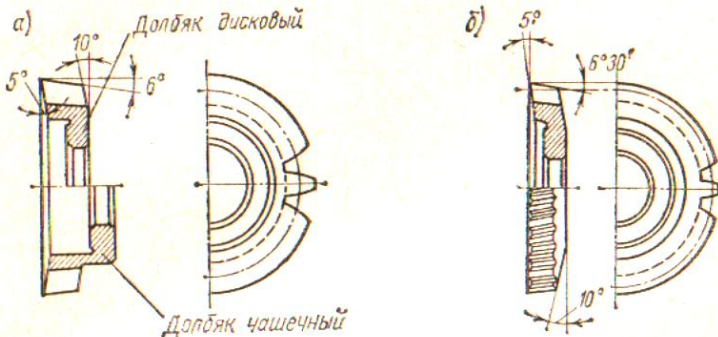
Виды долбяков: а-долбяк с прямыми зубьями; б- дискосозубый долбяк, для нарезания зубчатых колёс с косыми зубьями
